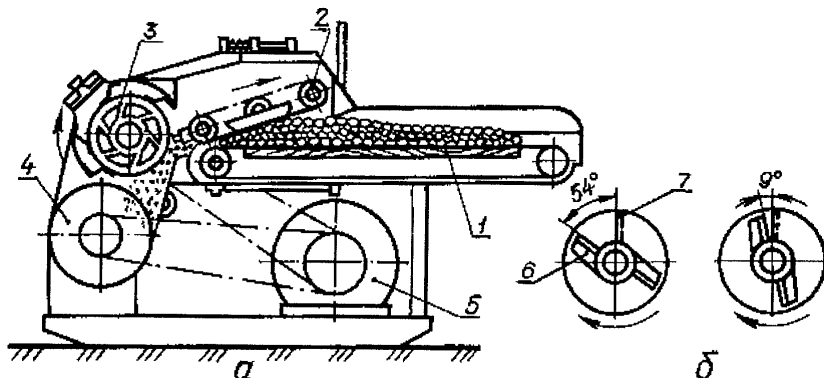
Подрібнювач кормів “Волгарь-5” (а) і схема регулювання ступеня подрібнення (б): 1 - транспортер подачі; 2 - ущільнюючий транспортер; 3 - ножовий барабан; 4 - плоскі ножі; 5 - електродвигун; 6 - лезо ножа; 7 - кромка шнека.
